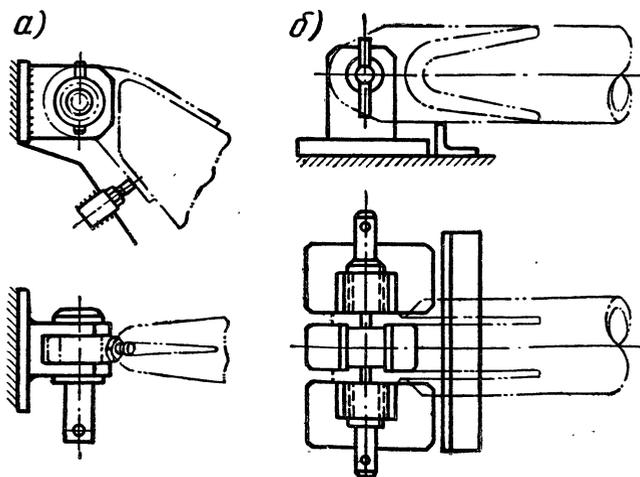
Фиксаторы для установки штампованных коробочек.
